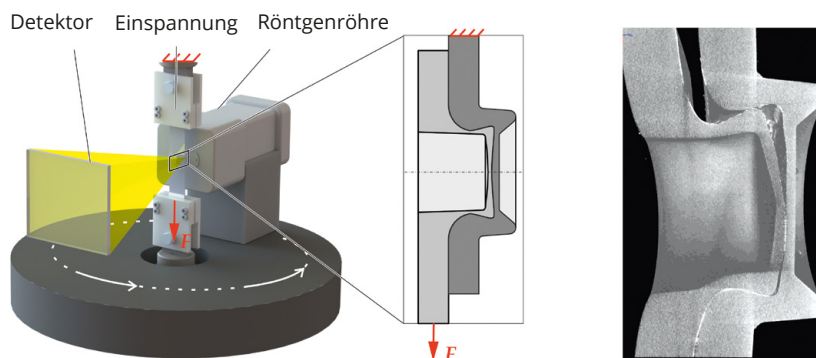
In-situ-Prüfaufbau (links) und rekonstruierte 3D-Abbildung einer Aluminium-Clinchverbindung unter Scherzugbelastung (rechts).
